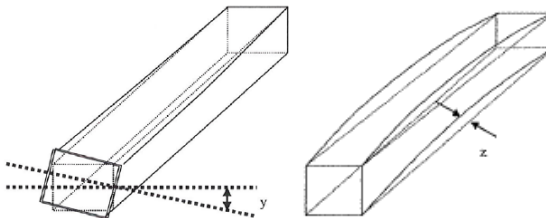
Скручування і кривизна (викривлення) заготовки
